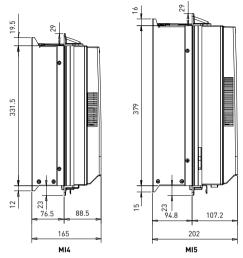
dimensions de profondeur en montage par bride, pour MI4 et MI5 (unité: mm)
